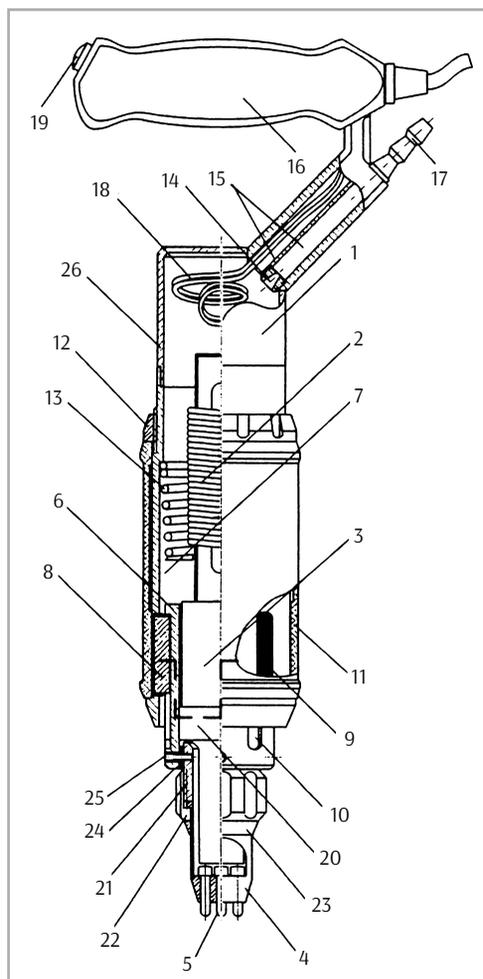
Конструкция ультразвукового виброударного инструмента: 1 — корпус; 2 — пьезоэлектрический преобразователь; 3 — волноводный акустический трансформатор; 4 — обойма-держатель бойков; 5 — бойки; 6 — втулка-держатель источника возбуждения; 7 — зазор; 8 — направляющие скольжения; 9, 10 — пазы для закладки направляющих; 11 — кожух; 12 — гайка; 13 — пружинный амортизатор; 14 — дроссель; 15 — канал для сжатого воздуха; 16 — рукоятка; 17 — штурцер; 18 — провода питания преобразователя; 19 — гашетка; 20 — фланец; 21 — переходная втулка; 22 — накидная гайка; 23 — стопорное кольцо; 24 — эластичная манжета; 25 — шпильки; 26 — разъёмное соединение
